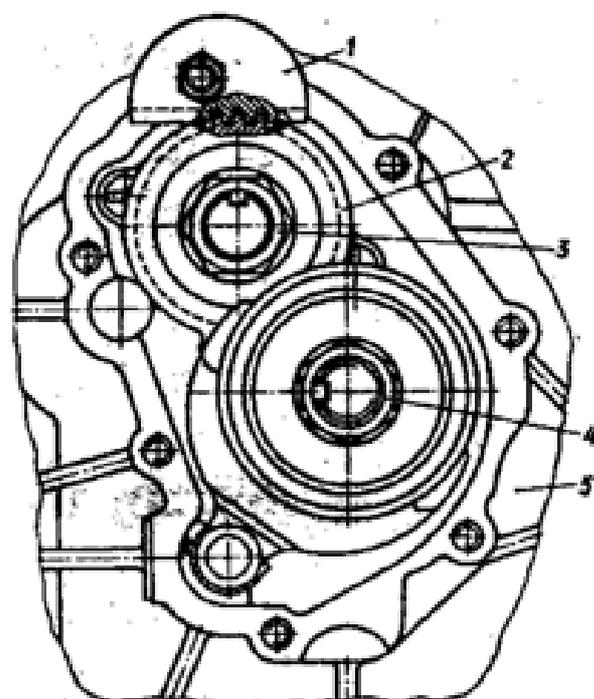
Стопорение пятой передачи коробки передач при отворачивании и заворачивании гаек ведущего и ведомого валов: 1 - стопор М9840-788; 2 - шестерня ведущая пятой передачи; 3, 4 - гайка ведущего и ведомого валов; 5 - картер коробки передач
